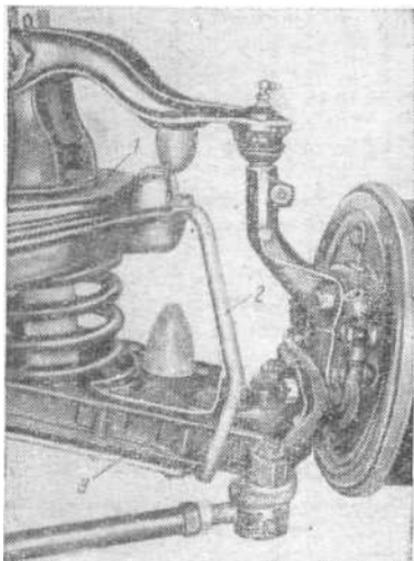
Установка предохранительной; стяжки для блокировки пружины передней подвески
